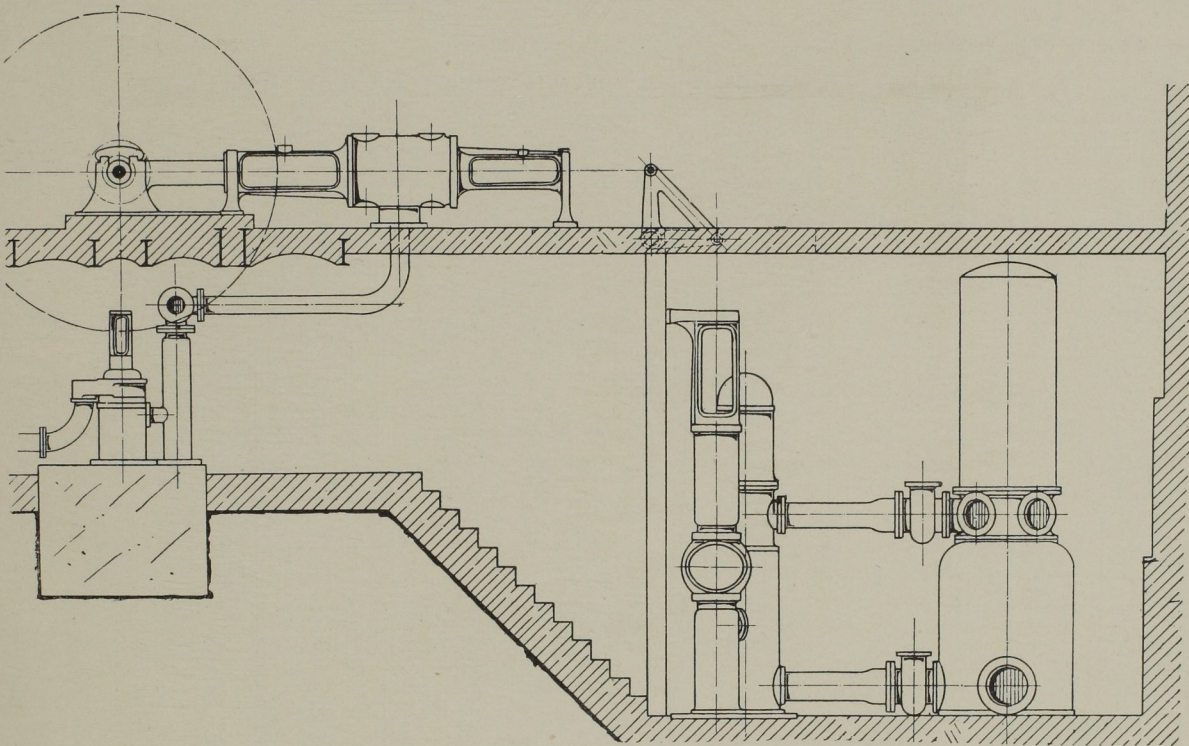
Seitenansicht der Pumpmaschine. Masst. 1:75.
